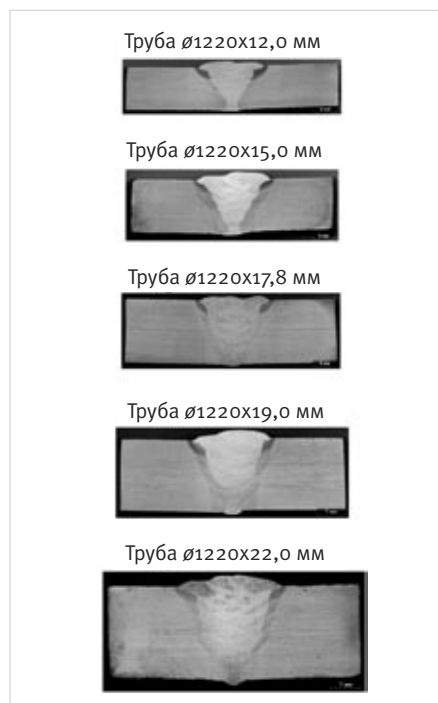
Макрошлифы из соединений, выполненных автоматической сваркой самозащитной порошковой проволокой
